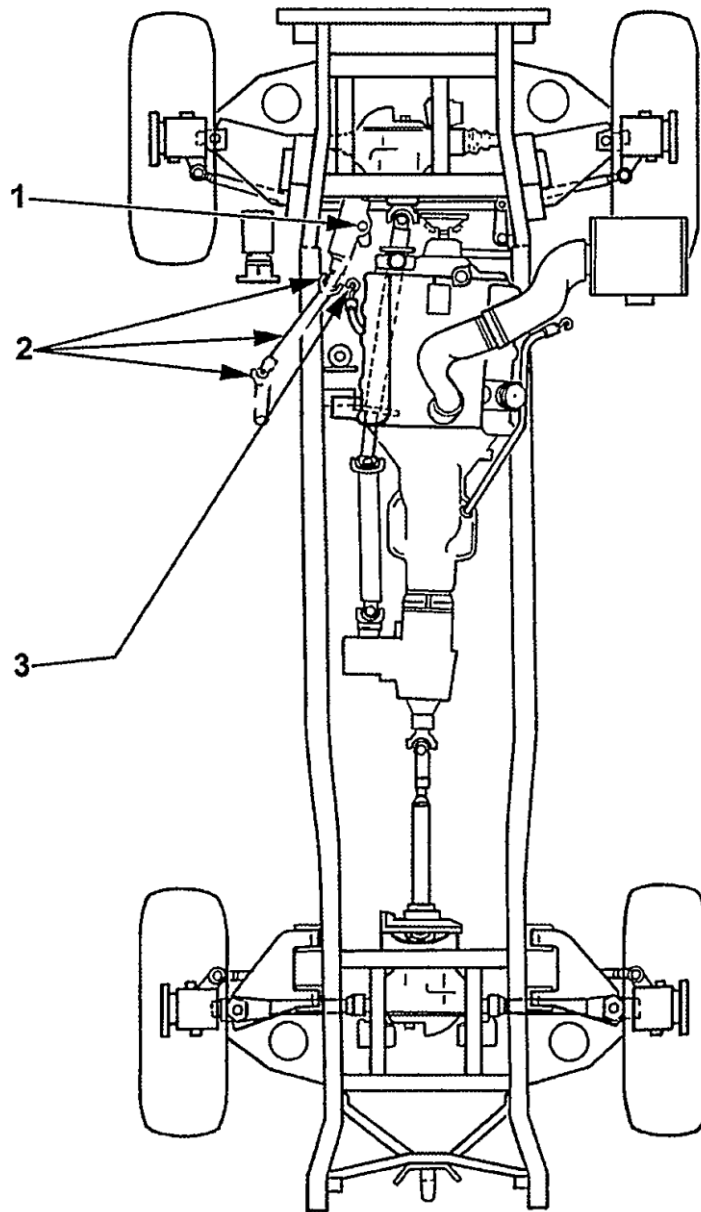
Точки змащування — з'єднувальна тяга, проміжний вал керування та картер двигуна.
